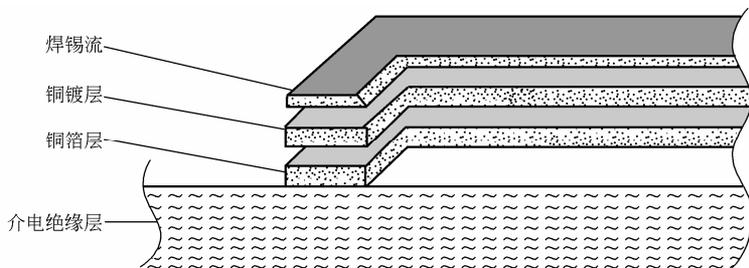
具有焊锡流的 PCB 铜层结构
